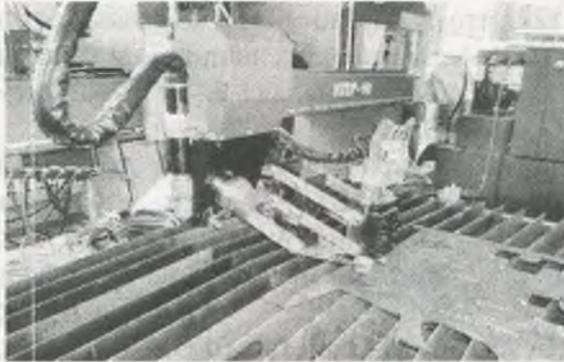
Система резки под углом криволинейных поверхностей плазменной головкой
